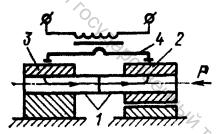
Схема стыковой сварки: 1 – свариваемые детали; 2, 3 – токоподводы; 4 – сварочный трансформатор
